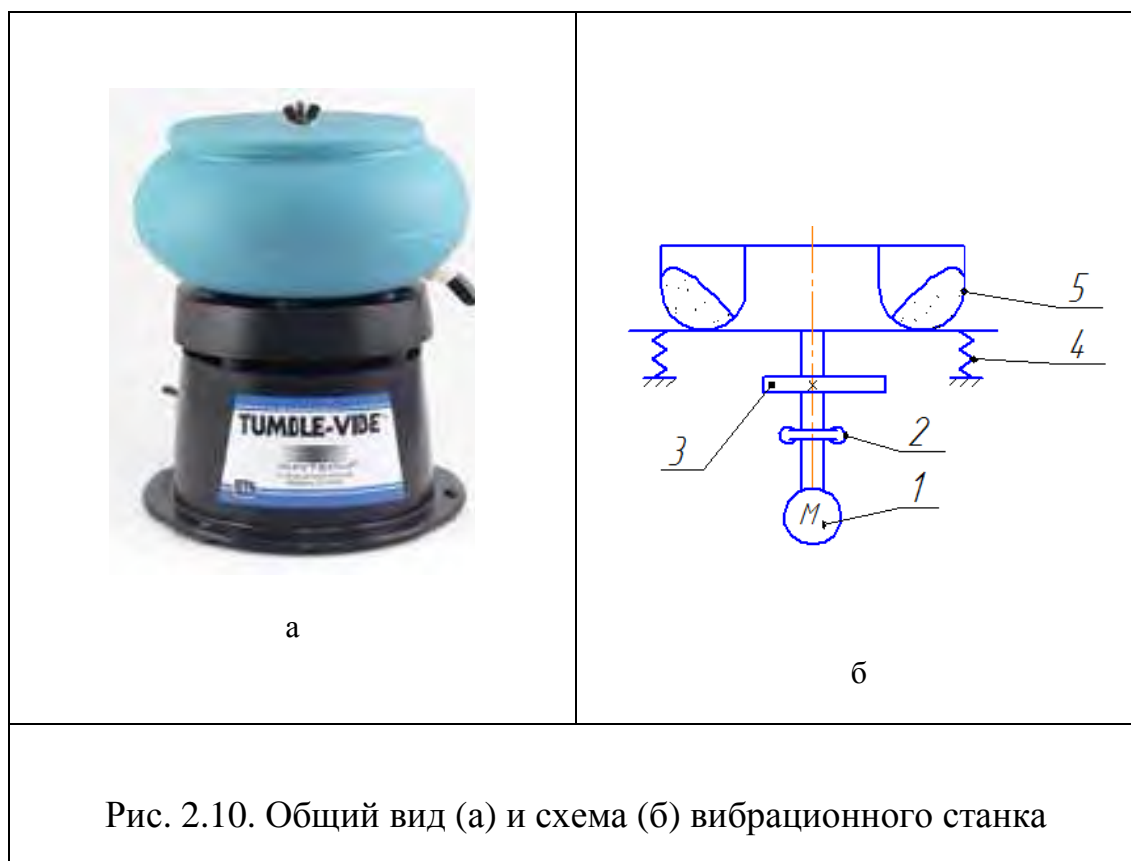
Общий вид (а) и схема (б) вибрационного станка
